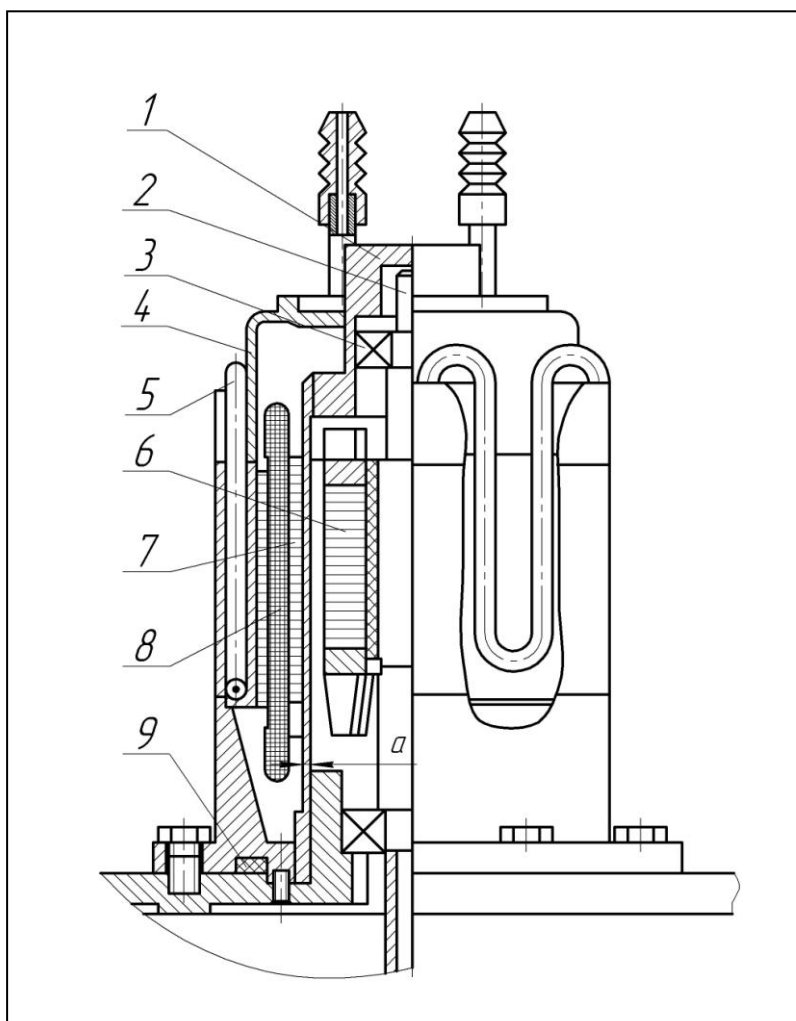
Электромагнитный ввод вращения в вакуум на базе асинхронного двигателя: 1 – глухой герметичный стакан; 2 – вал двигателя; 3 – шарикоподшипник; 4 – корпус статора; 5 – трубка принудительного охлаждения; 6 – ротор; 7 – тонкая герметичная немагнитная стенка; 8 – обмотка статора; 9 – присоединительное уплотнение
